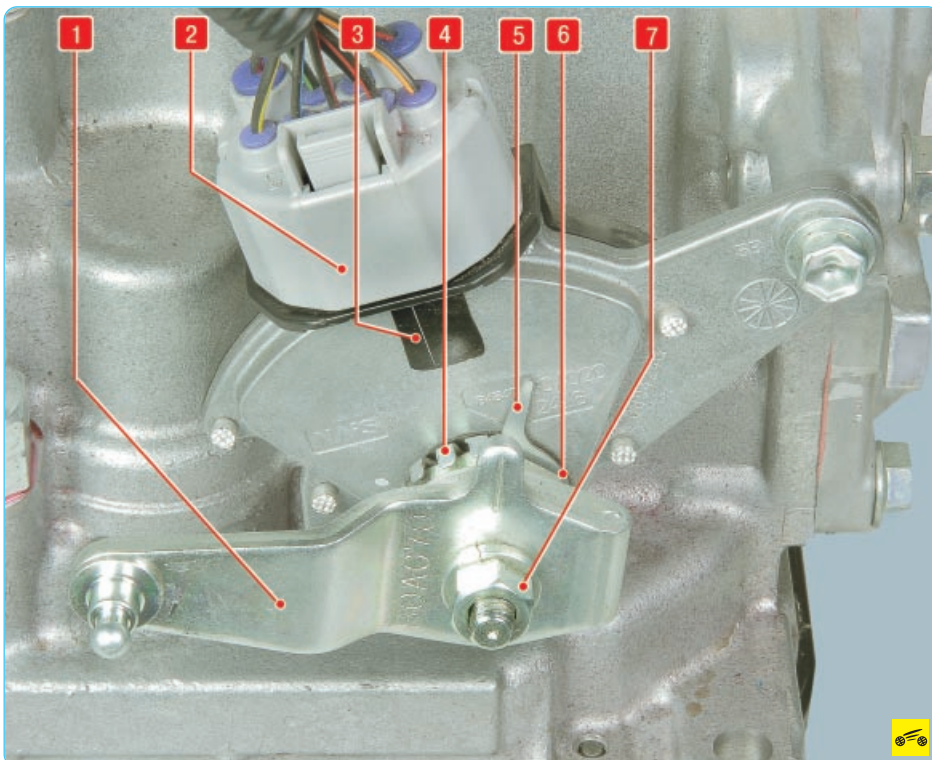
Датчик положения селектора автоматической коробки передач: 1 – рычаг переключения передач; 2 – колодка жгута проводов; 3 – линия нейтралей; 4 – стопорная шайба; 5 – язычок стопорной шайбы; 6 – контргайка; 7 – гайка
